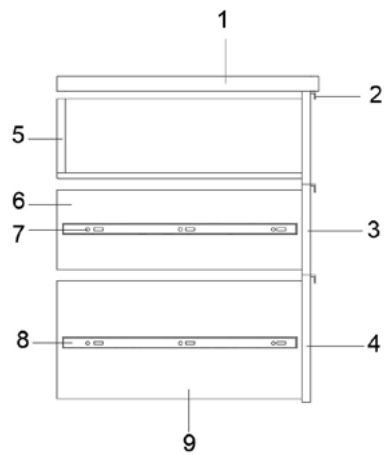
Detalle constructivo cajonera HDPE reciclado
